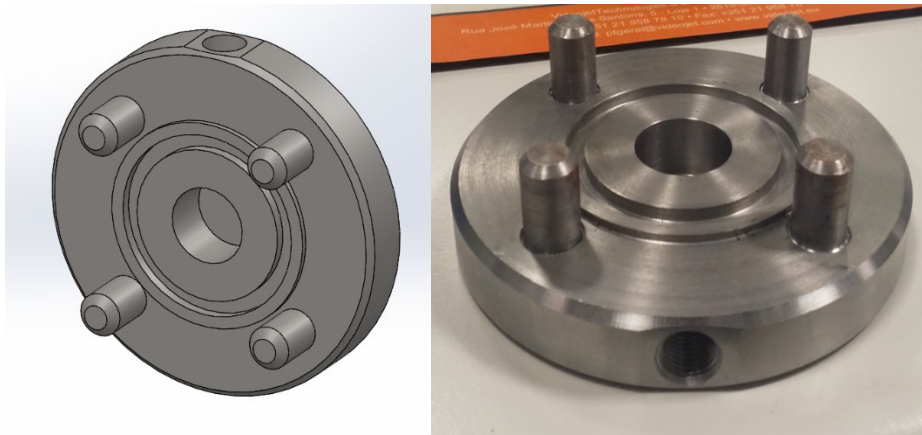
Flanges fabricadas para realizar o teste de fuga.
